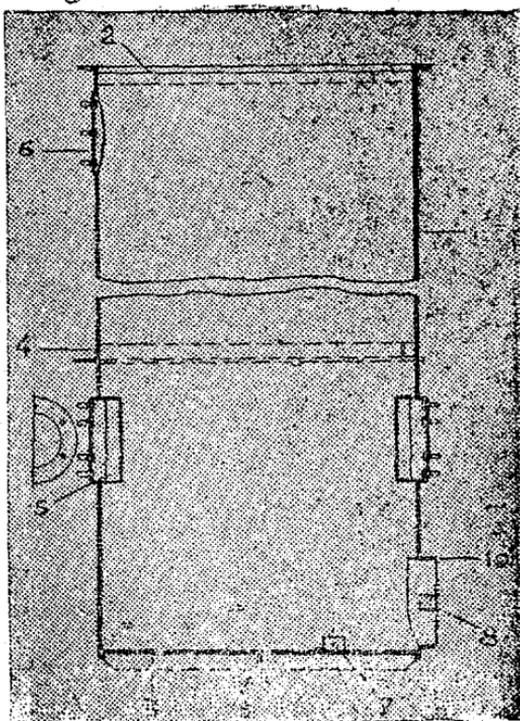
Корпус газогенератора в сборе: 1—корпус; 2—фланец корпуса; 3—дно корпуса; 4—пояс крепления газогенератора; 5—коробка воздушного клапана; 6—фланец отбора газа; 7—упор для опоры колосниковой решетки; 8—ушко траверсы зольникового люка; 9—ребра жесткости днища; 10—горловина зольникового люка.
